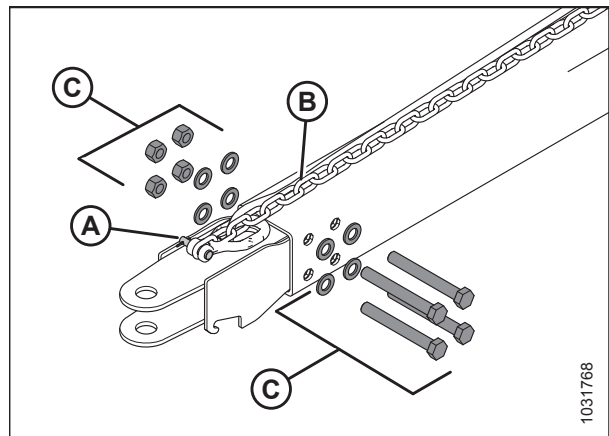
Extracción del adaptador de remolque de la horquilla
